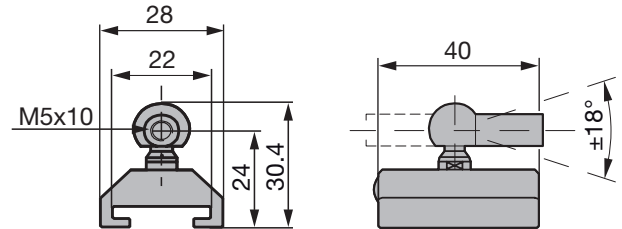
Medidas de montaje del sensor de posición BTL5-F-2814-1S
